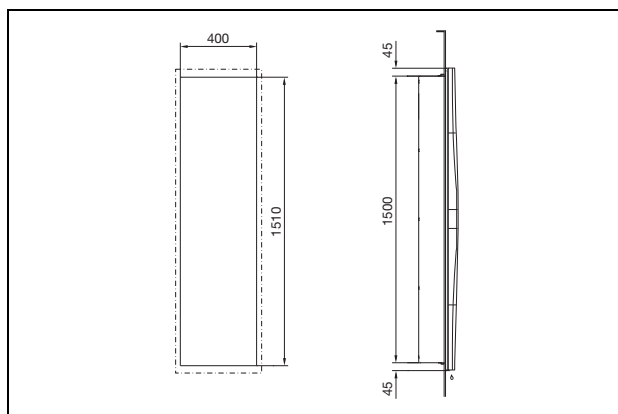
SK 3303.xxx, SK 3361.xxx vnitřní montáž
